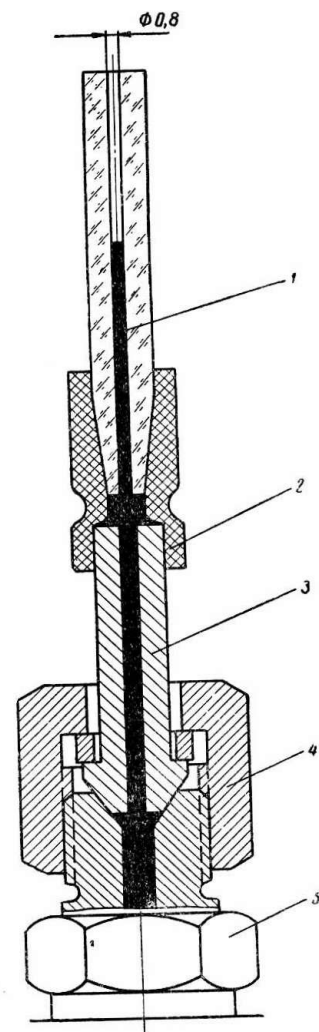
Приспособление для проверки угла опережения подачи топлива:
